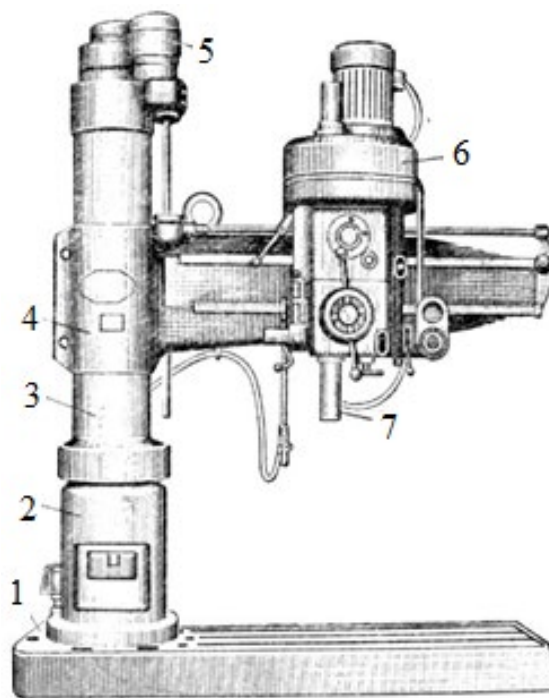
Загальний вигляд радіально-свердлильного верстата:
